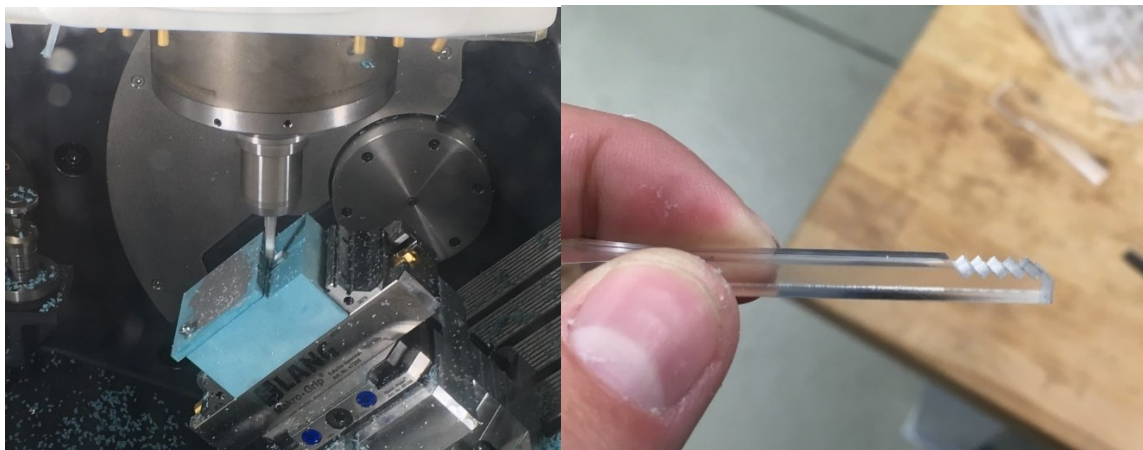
Návrh a následné frézování přípravku pro zajištění zkušebních vzorků
